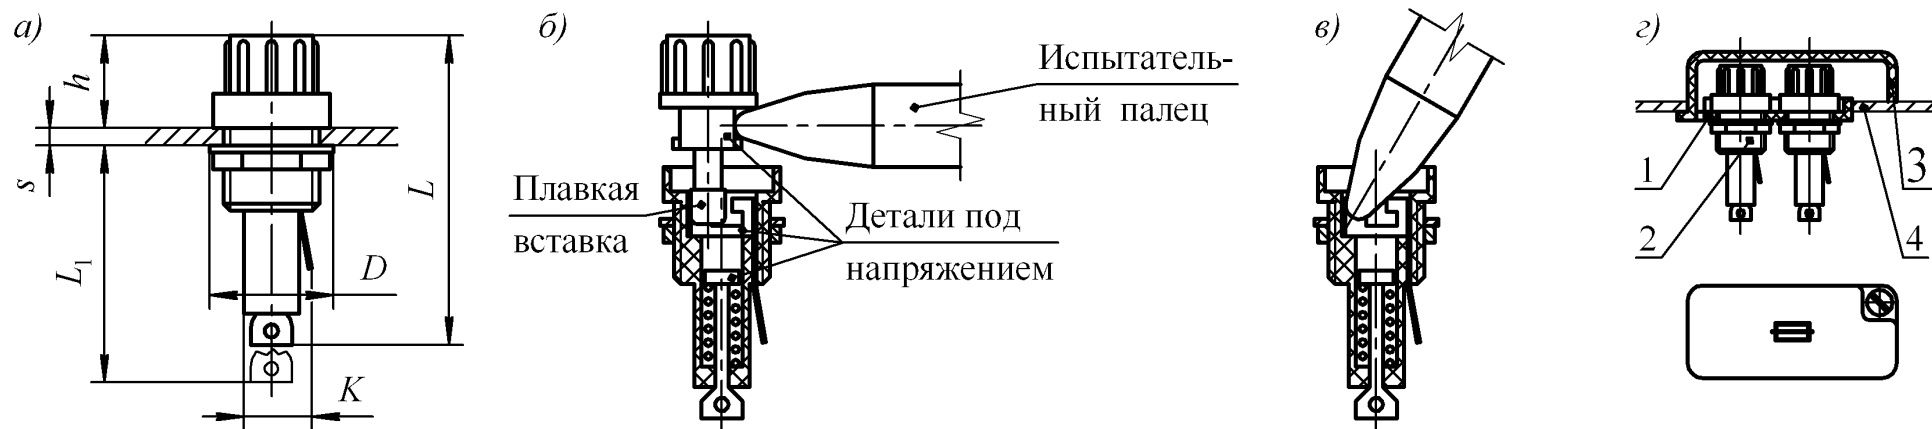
Держатель плавкой вставки ДВП4: а) внешний вид и размеры; б) и в) проверка доступности частей под напряжением; г) установка держателей плавких вставок в изолирующей коробке.
